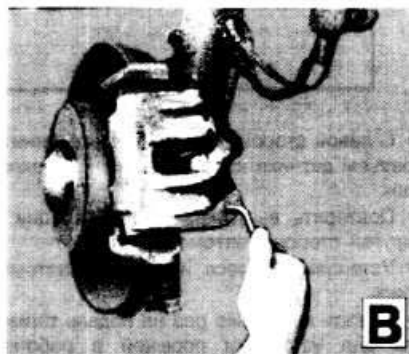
Замена колодок тормозного механизма переднего колеса:
